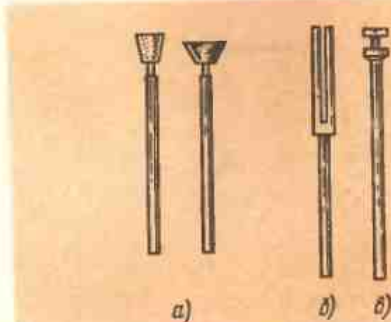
Инструмент для борманины: а — головки фасонные шлифовальные № 2 (слева) и № 3; б — оправка для абразивной шкурки, в — оправка для дисковых кругов
